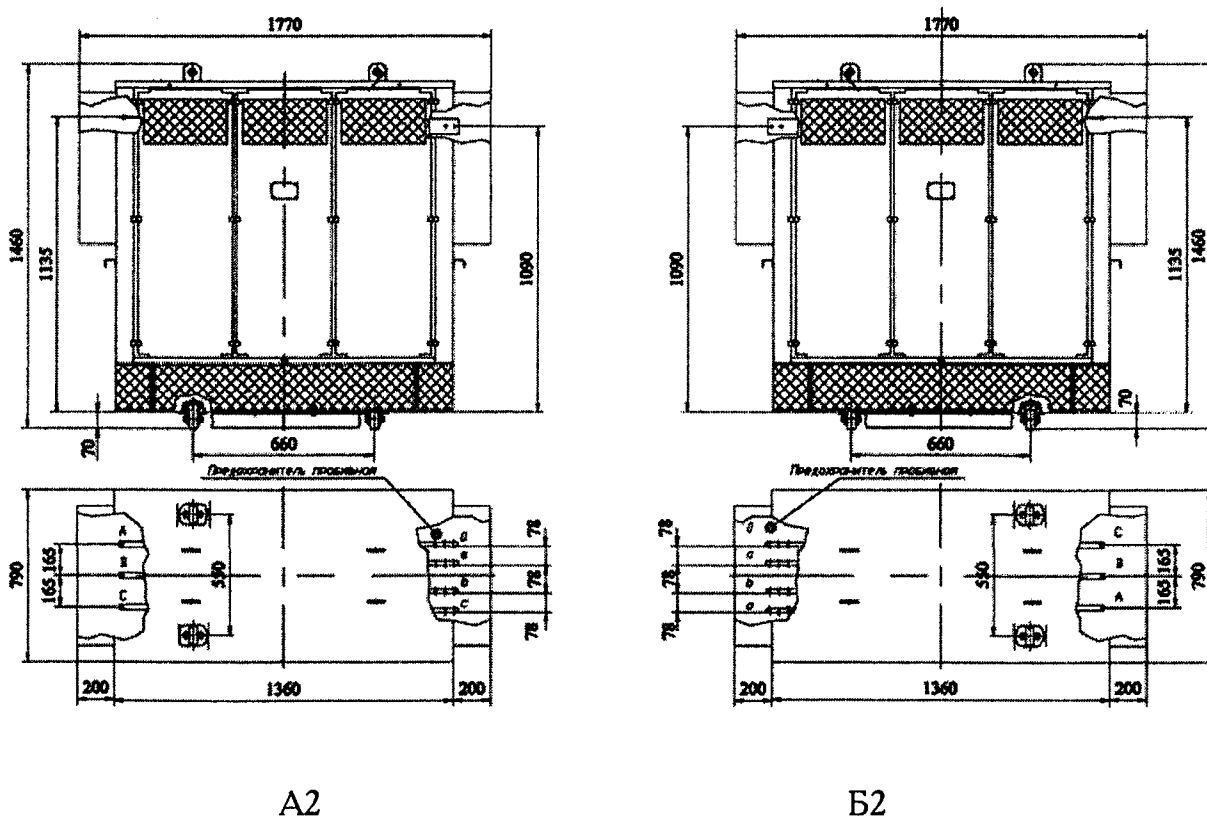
Габаритные, установочные, присоединительные размеры трансформатора ТСЗФ-160/10 УЗ (сторона подключения: А2 - левая, Б2 - правая)
